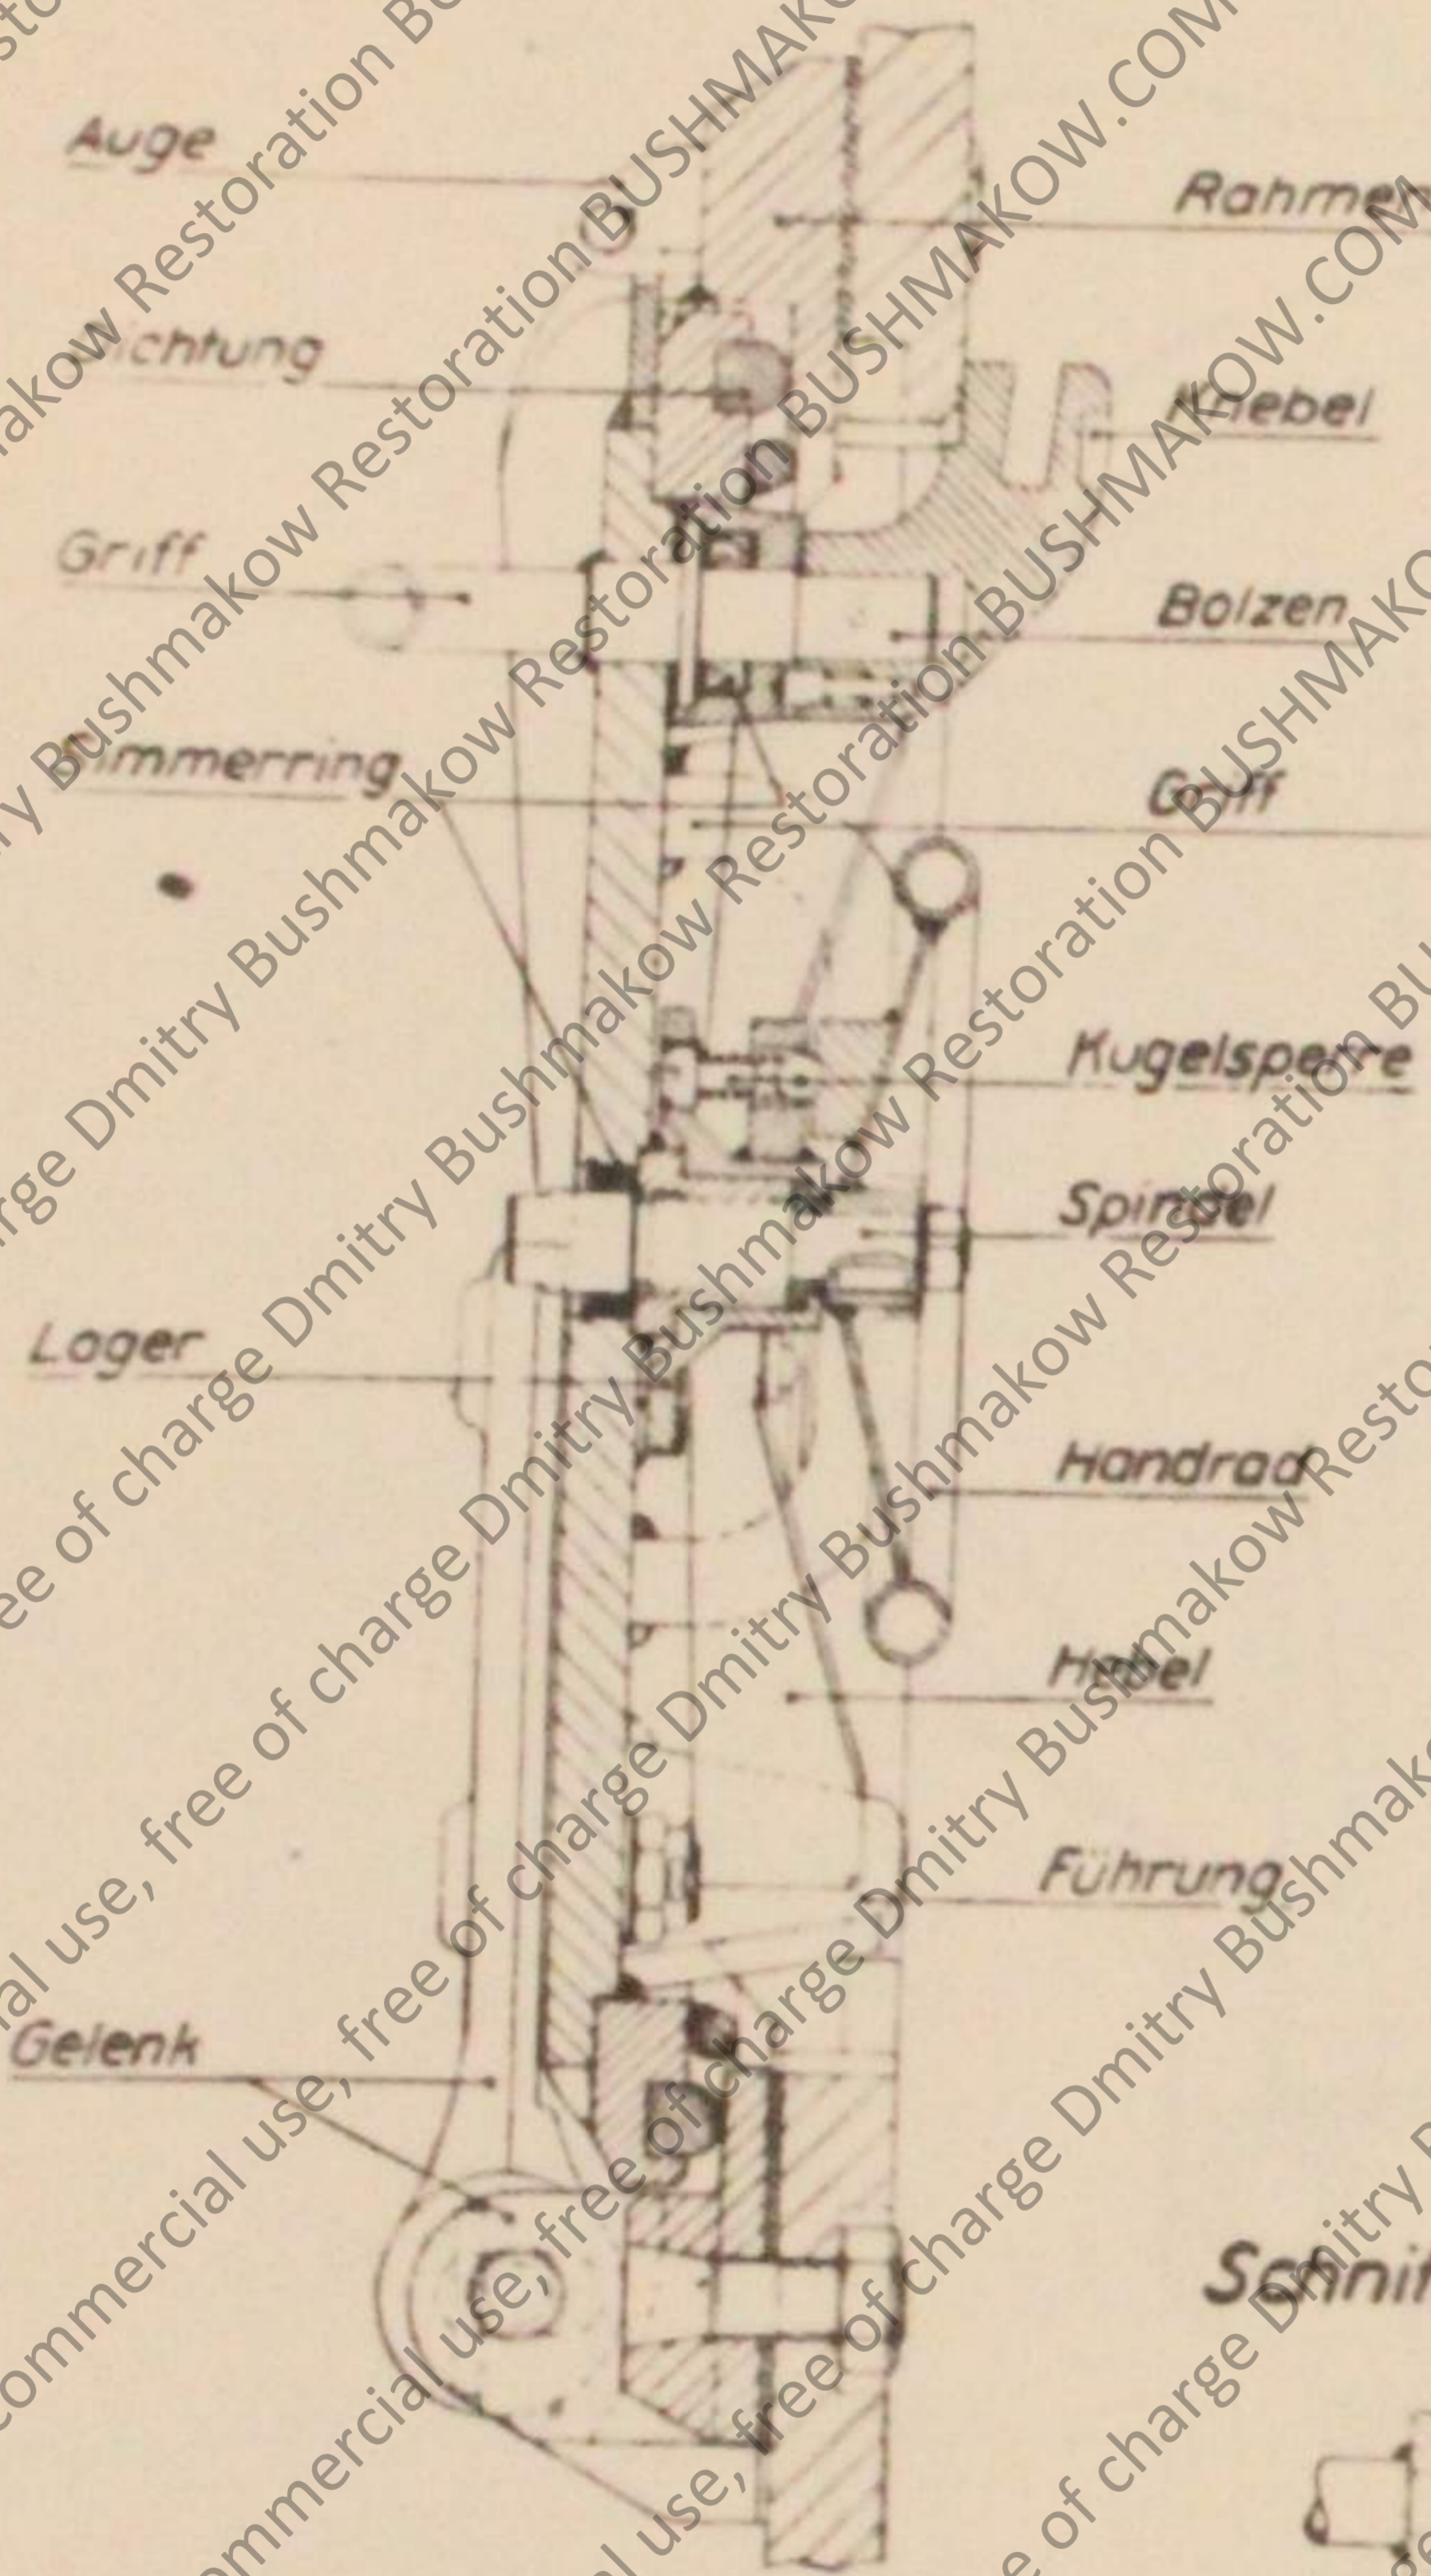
Ladeschutzschlüsseldeckel, alte Bauart
